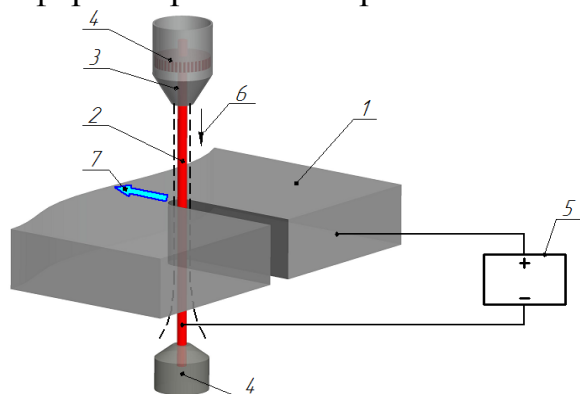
Схема электрохимической обработки движущимся ПЭИ: 1 – обрабатываемая заготовка; 2 – проволочный электрод инструмент; 3 – сопло; 4 – электрододержатель; 5 – источник питания; 6 – направление подачи электролита; 7 – направление перемещения ПЭИ
